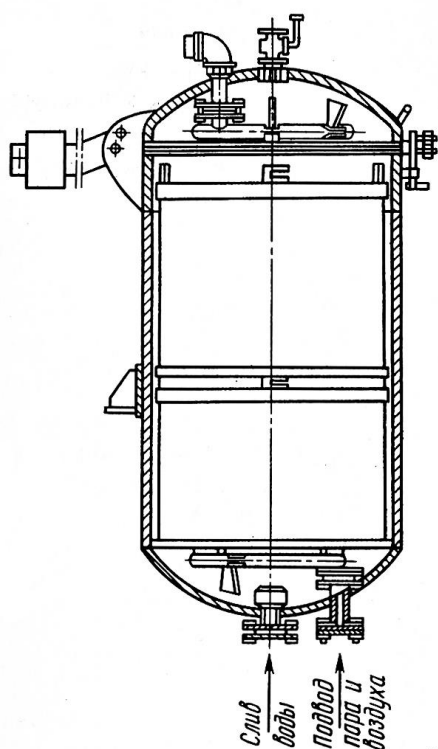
Схема коммуникаций автоклава: 1 – корпус автоклава; 2 – термометрическая коробка с циркуляционной трубой; 3 – продувочный кран; 4 – сливные вентили; 5 – обратный клапан; 6 – барботер
